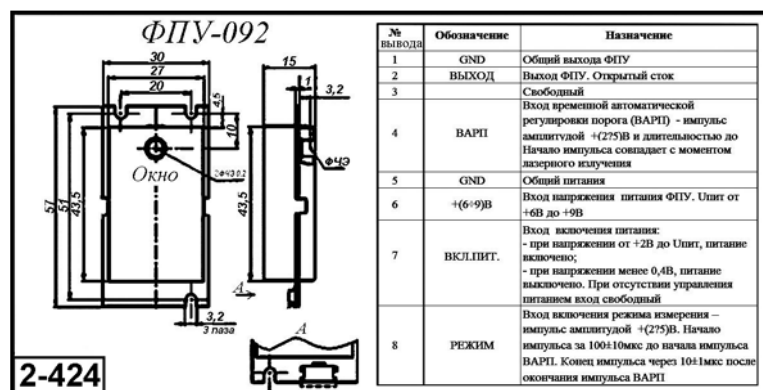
Внешний вид, габаритные размеры и таблица назначения выводов ФПУ-092
